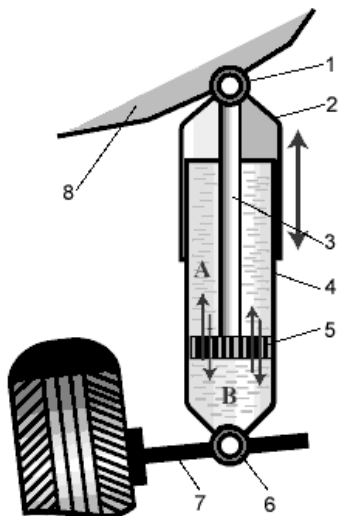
Схема амортизатора 1 - верхняя проушина; 2 - защитный кожух; 3 - шток; 4 - цилиндр; 5 - поршень с клапанами сжатия и «отбоя»; 6 - нижняя проушина; 7 - ось колеса; 8 - кузов автомобиля
